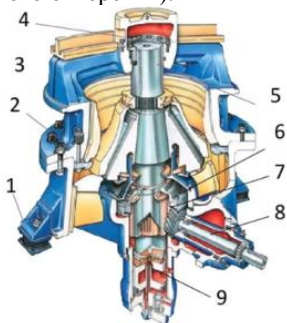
Конусная дробилка(ККД): 1-станина; 2-неподвижный конус; 3-подвижный конус; 4-траверса; 5-вертикальный вал; 6-колесо коническое; 7-эксцентриковая втулка; 8-ведущий вал; 9-стакан.
